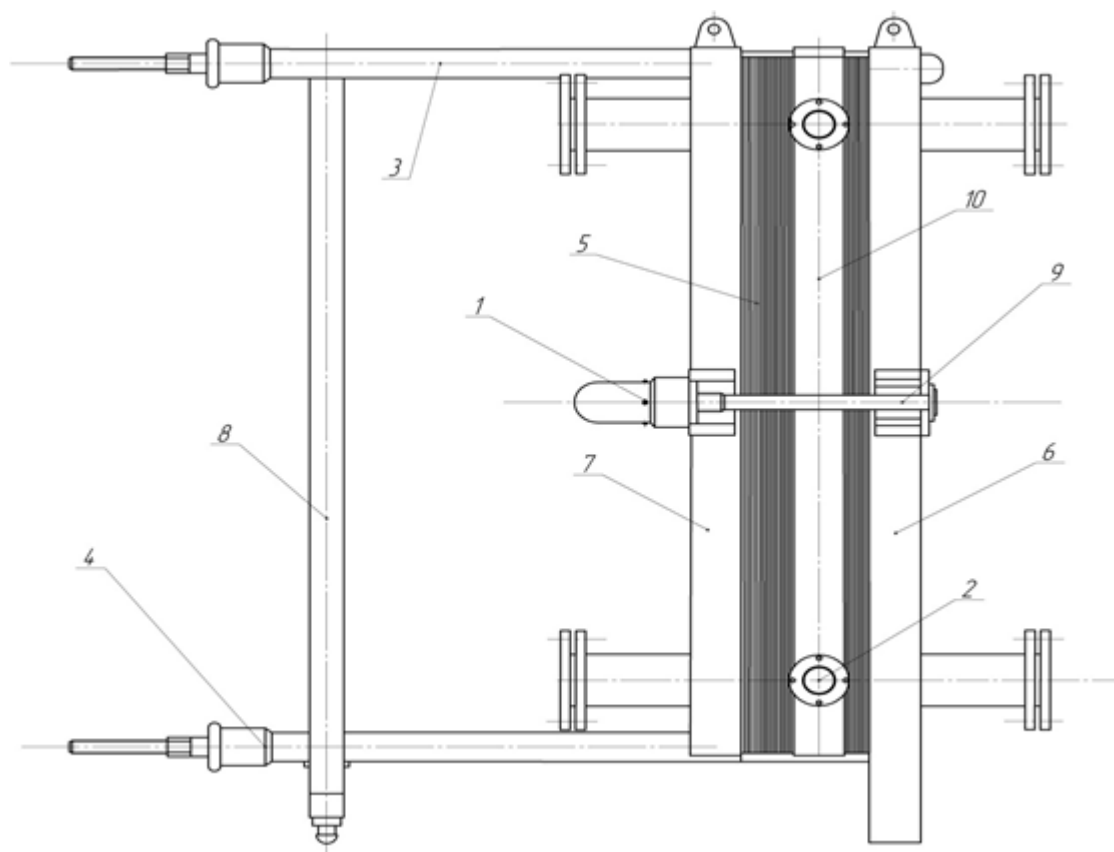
Пластинчатий теплообмінник: 1 - нажимна гайка; 2 - штуцер; 3 - верхня штанга; 4 - нижня штанга; 5 - пластина; 6 - нерухома опорна плита; 7 - рухома опорна плита; 8 - кінцева стійка; 9 - стержень, 10 - проміжна плита.
